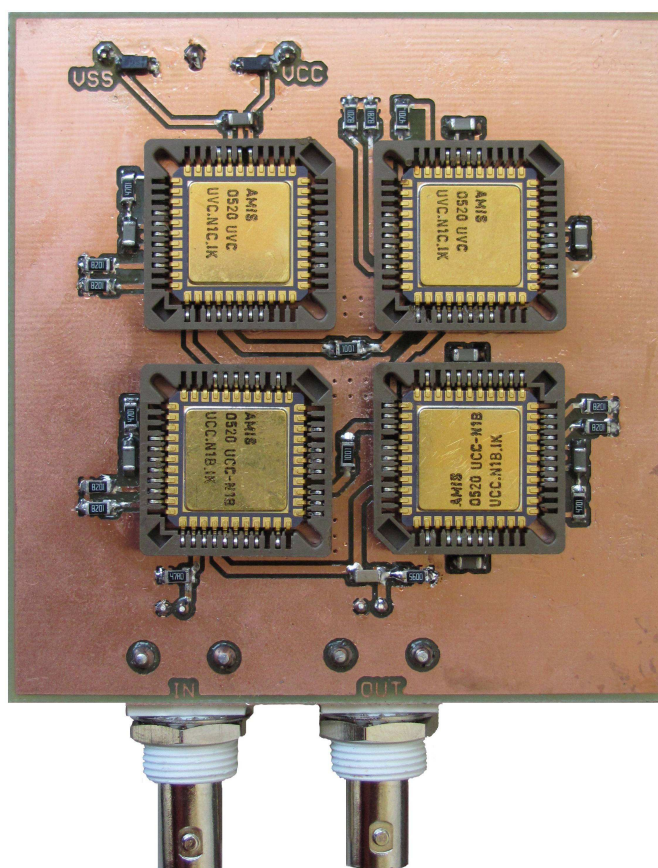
Rozmístění součástek strana BOTTOM
